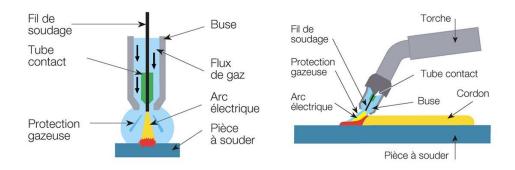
Principe de Soudage MIG/MAG [14]
